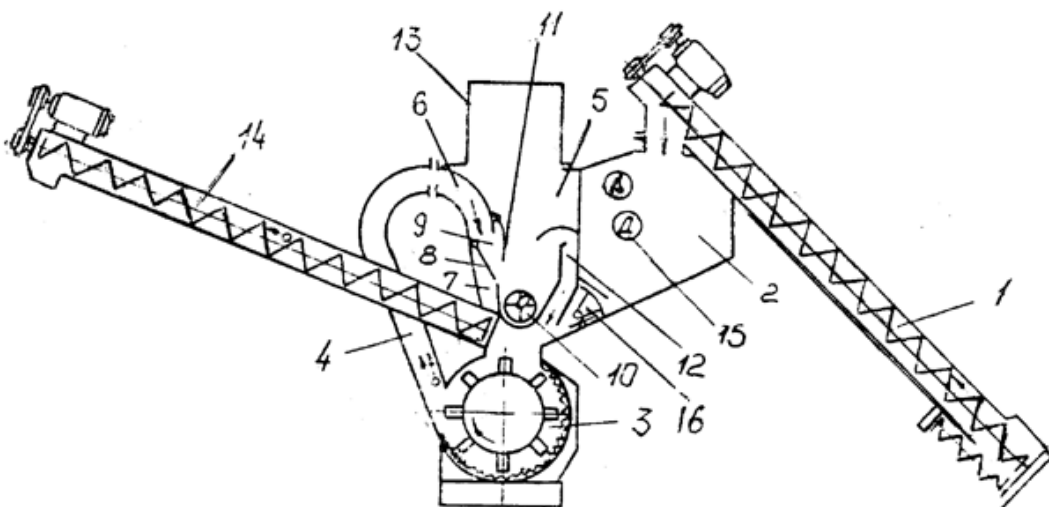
Технологічна схема дробарки ДБ -5: 1- шнек завантажувальний; 2- бункер; 3- камера подрібнювання; 4- кормопровід; 5- розподільна камера; 6- дефлектор; 7- зворотній канал; 8- заслінка; 9- вікно для проходу готового продукту; 10- шнек дробарки; 11- козирок; 12- рециркуляційний канал для повітря; 13- фільтр; 14- вивантажувальний шнек; 15- датчики верхнього і нижнього рівнів; 16- заслінка.
